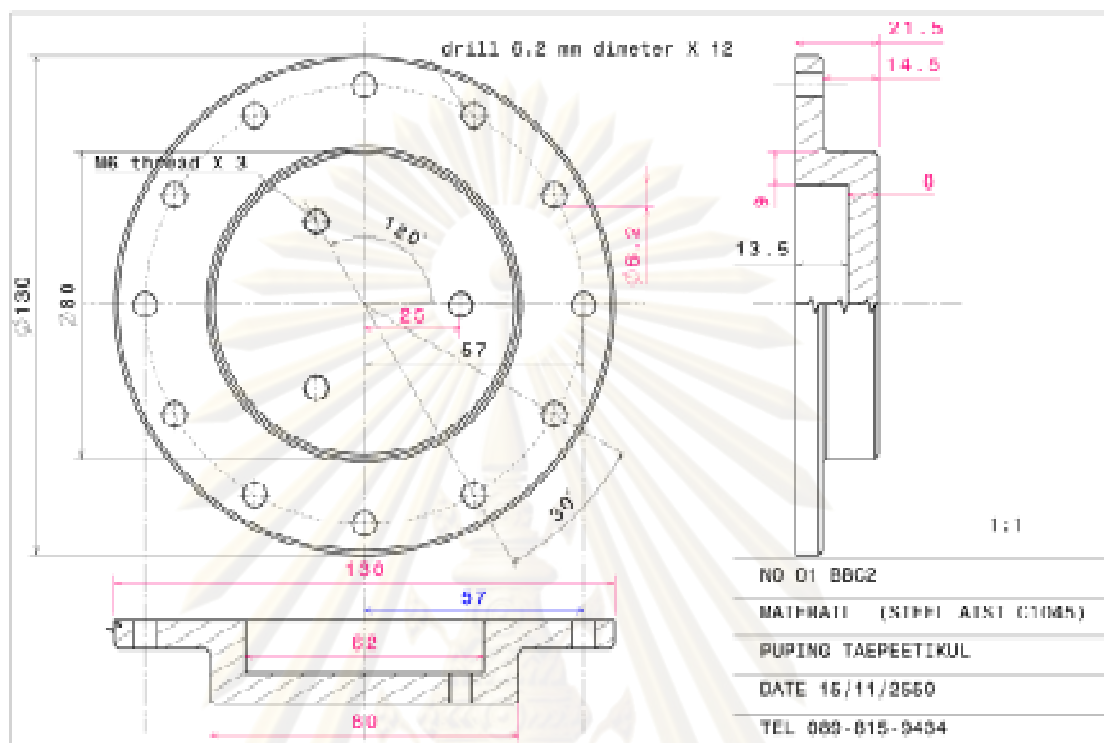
แบบ Drawing ของ MCHP ด้าน Top side view
